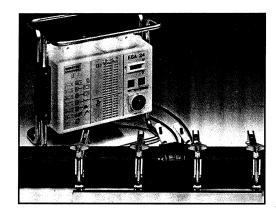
لحام المواسير باللحام المتقابل (Butt Welding)
